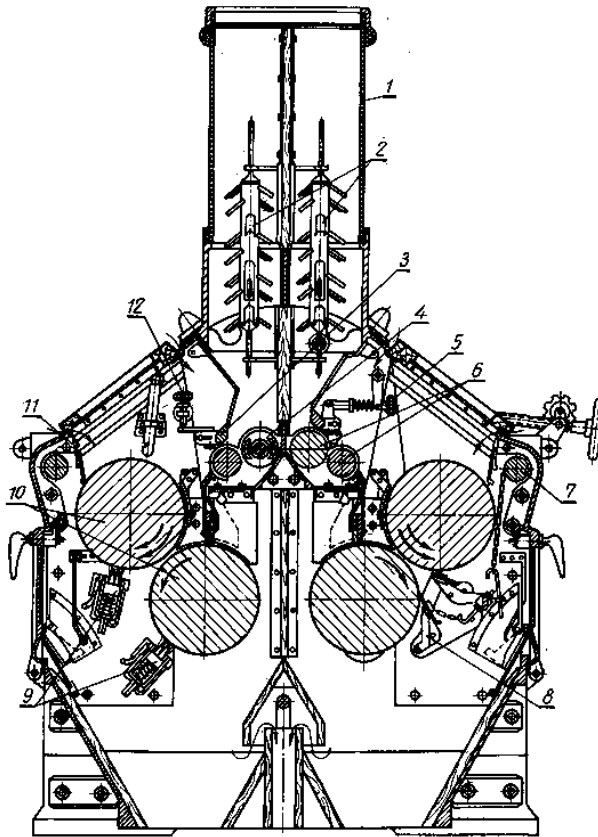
Вальцевий станок ЗМ: 1 – труба живильна; 2 – поплавці; 3 – заслінка секторна; 4 – шнек-побудник; 5 – механізм автоматичного відкриття заслінки; 6 – живильні валки; 7 – вал привально-відвальний; 8 – ножовий механізм; 9 – щітки; 10 – вальці; 11 – щілина аспіраційна; 12 – механізм регулювання живлення
